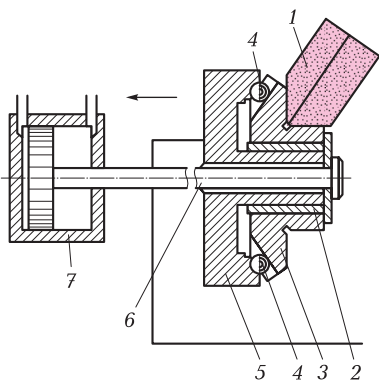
Схема обработки поверхностей круглым наружным шлифовальным кругом с угловым расположением шлифовального круга
